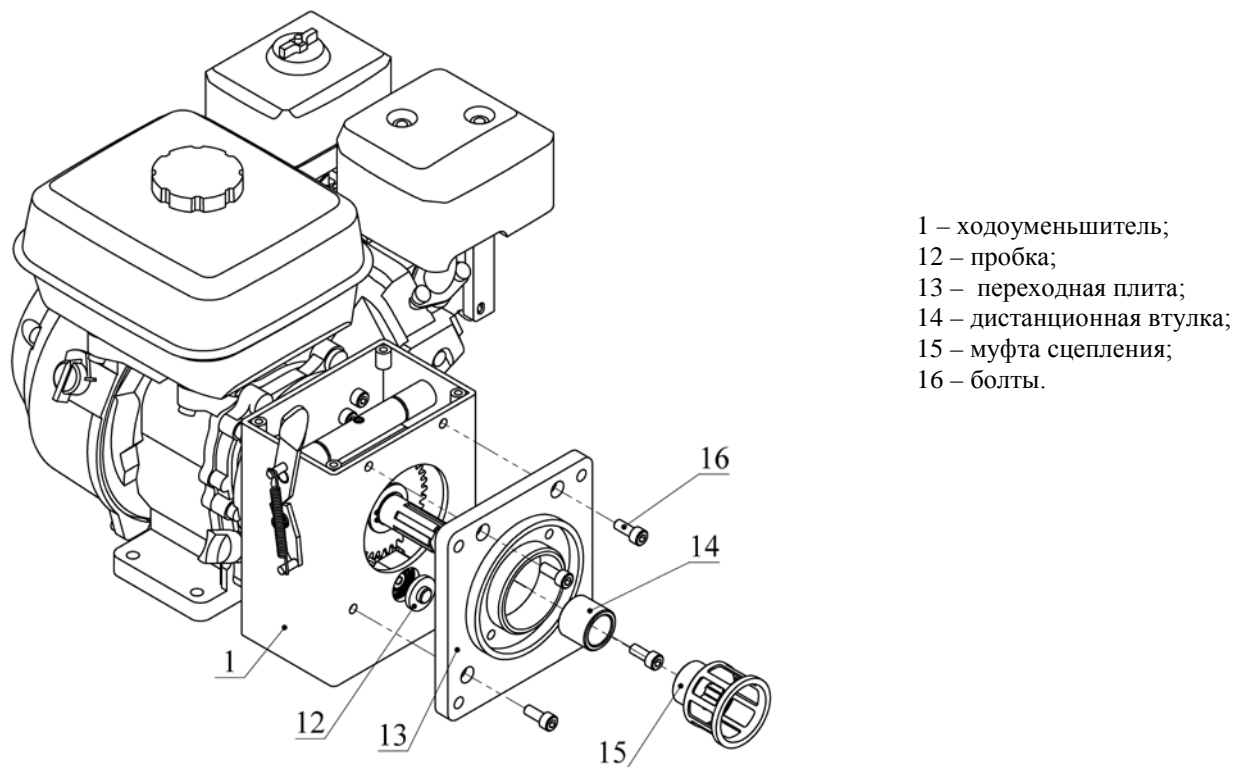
Схема установки переходной плиты мотоблока на ходоуменьшитель
